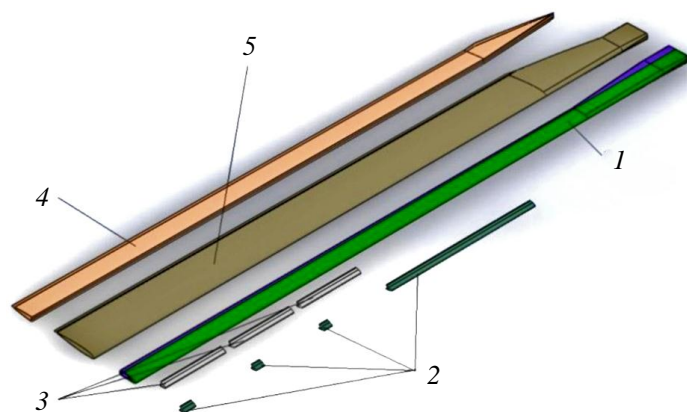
Конструкция лопасти из стеклопластика для БПЛА вертолетного типа:
